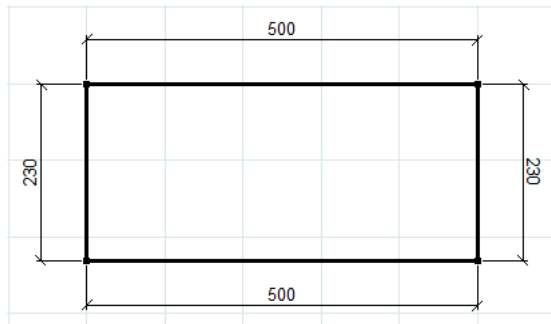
Заготовка нижньої горизонтальної полички (габаритні розміри)
